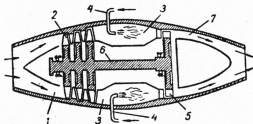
Схема турбореактивного двигателя с осевым компрессором:
